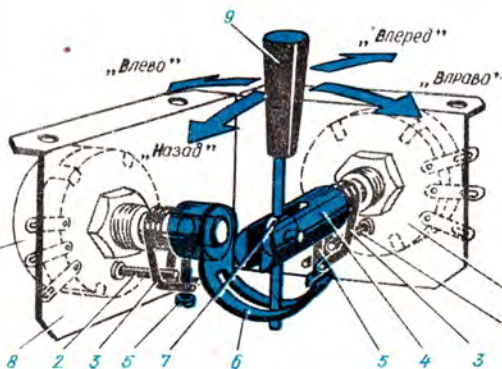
Механизм управления: 1 — переменные резисторы (R_2 , R_6); 2 — упоры; 3 — возвратные пружины; 4 — соединительная втулка; 5 — стопорные винты; 6 — поводок; 7 — рычаг; 8 — корпус; 9 — ручка управления.
